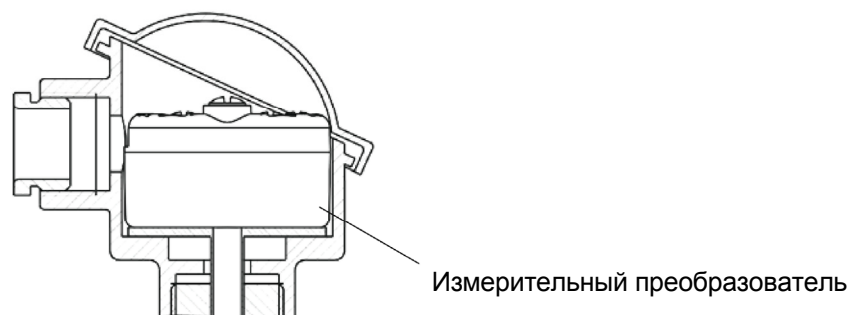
Крепление измерительного преобразователя в основании соединительной головки
